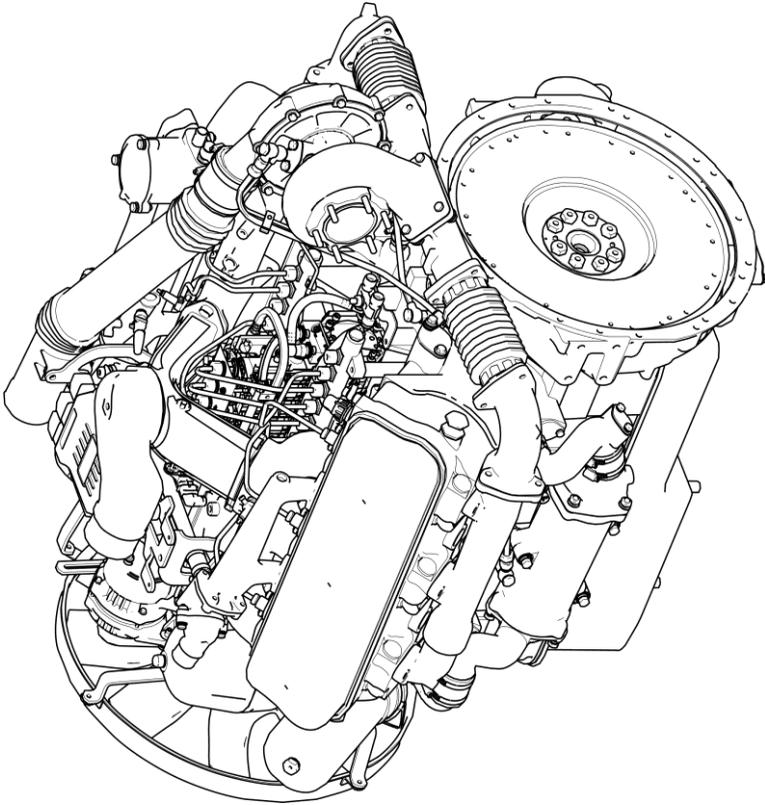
а – Двигатель ЯМЗ-6565 (общий вид слева)
